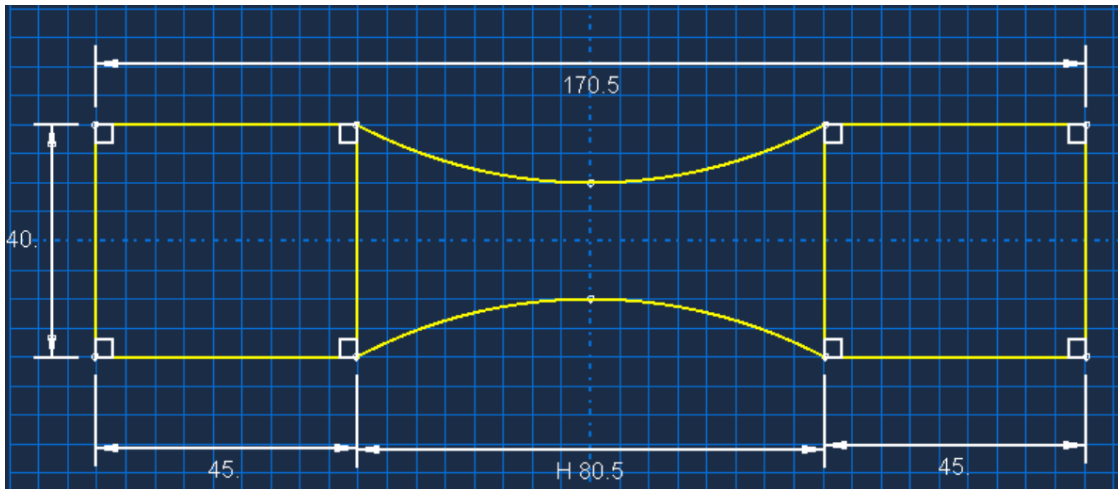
Dimensions des éprouvettes sans soudage.
